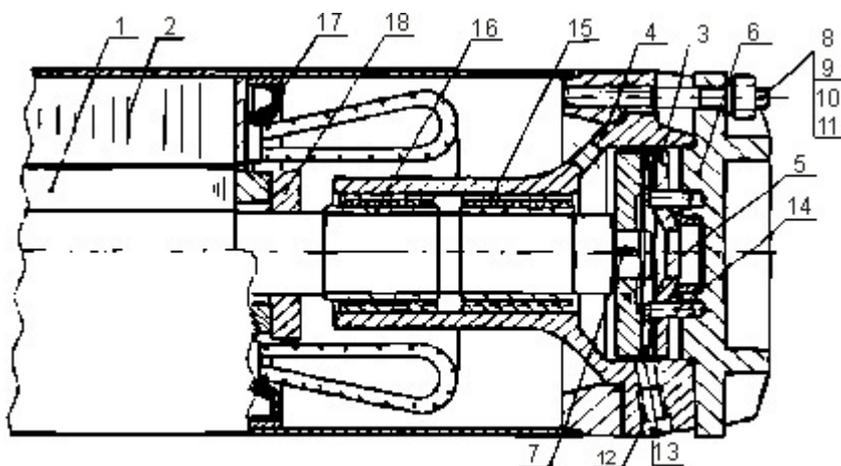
Электродвигатель погружной: 1 — ротор; 2 — статор; 3 — подпятник; 4 — щит подшипниковый; 5 — пята; 6 — днище; 7 — шпонка; 8 — шпилька; 9 — гайка; 10, 11 — шайбы; 12 — кольцо уплотнительное; 13 — пробка; 14 — штифт; 15 — подшипник резинометаллический; 16 — втулка ротора; 17 — кольцо защитное; 18 — кольцо балансировочное из сплава
